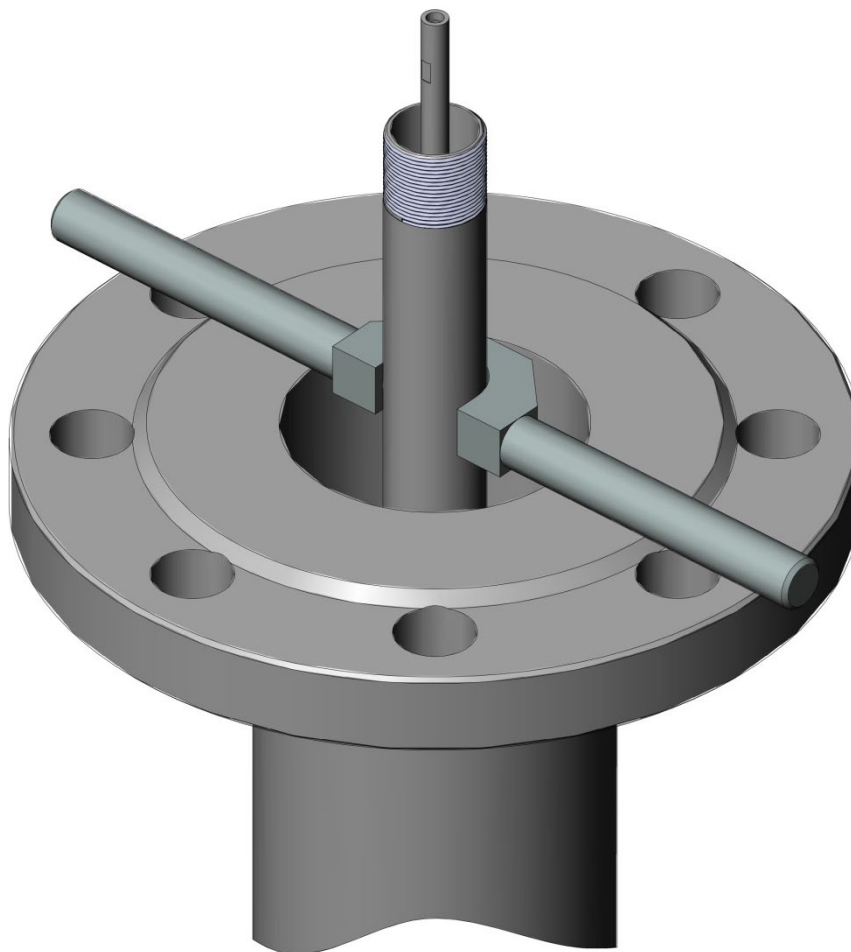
Погружение средней секции в резервуар с опорой на верхнее приспособление
